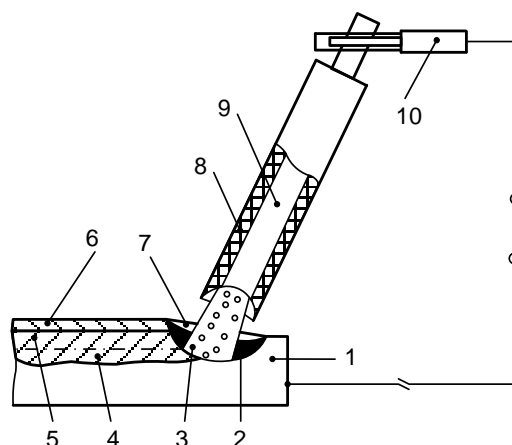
Ручная дуговая сварка штучным электродом: 1 – основной металл; 2 – сварочная ванна; 3 – электрическая дуга; 4 – проплавленный металл; 5 – наплавленный металл; 6 – шлаковая корка; 7 – жидкий шлак; 8 – электродное покрытие; 9 – металлический стержень электрода; 10 – электрододержатель
